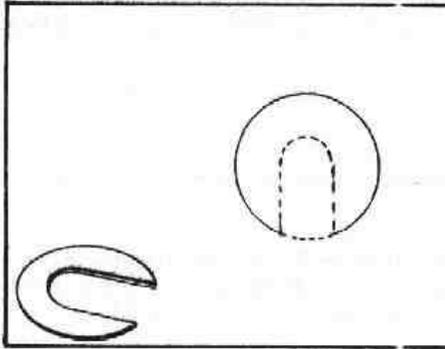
Placa extractora para desmontaje de la polea del -
